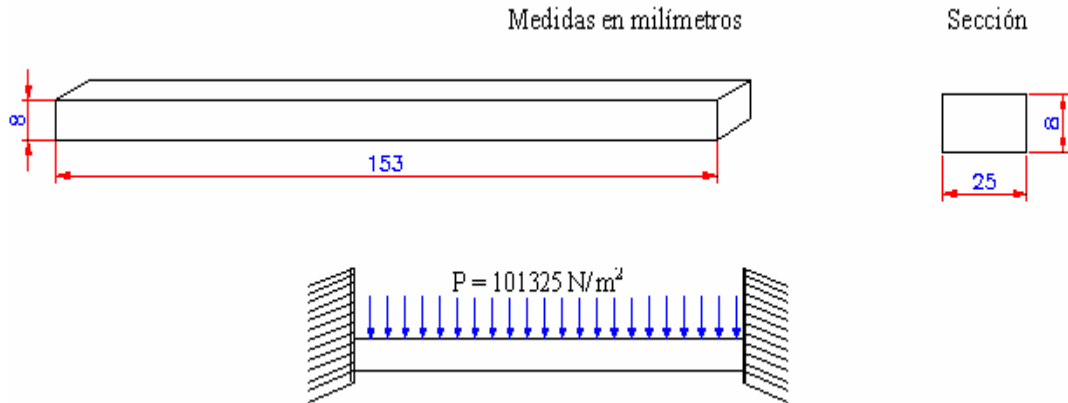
Geometría y semejanza con una viga doblemente empotrada
